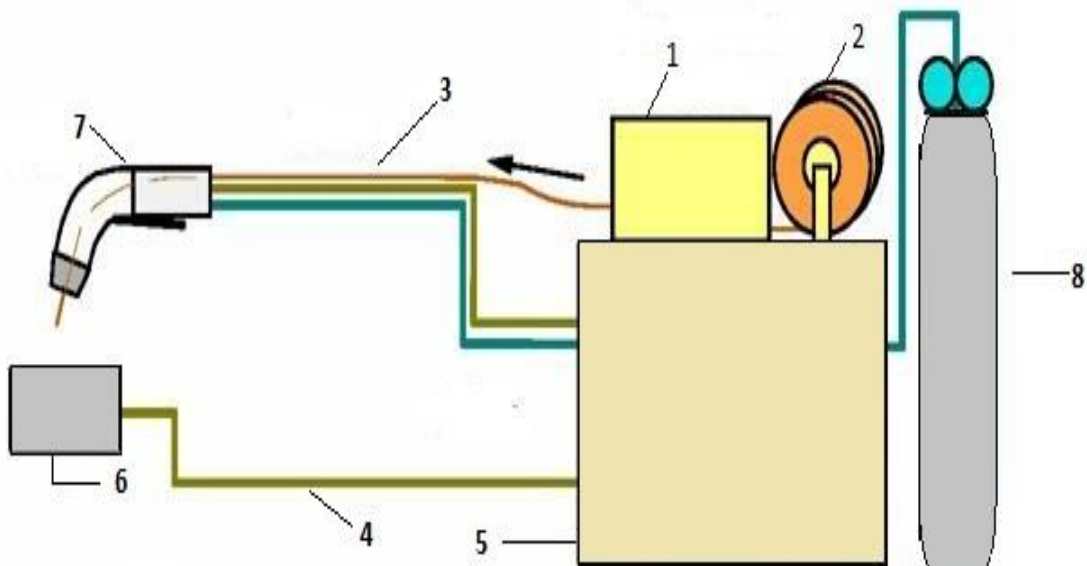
Esquema de uma máquina de soldadura MAG[13]
